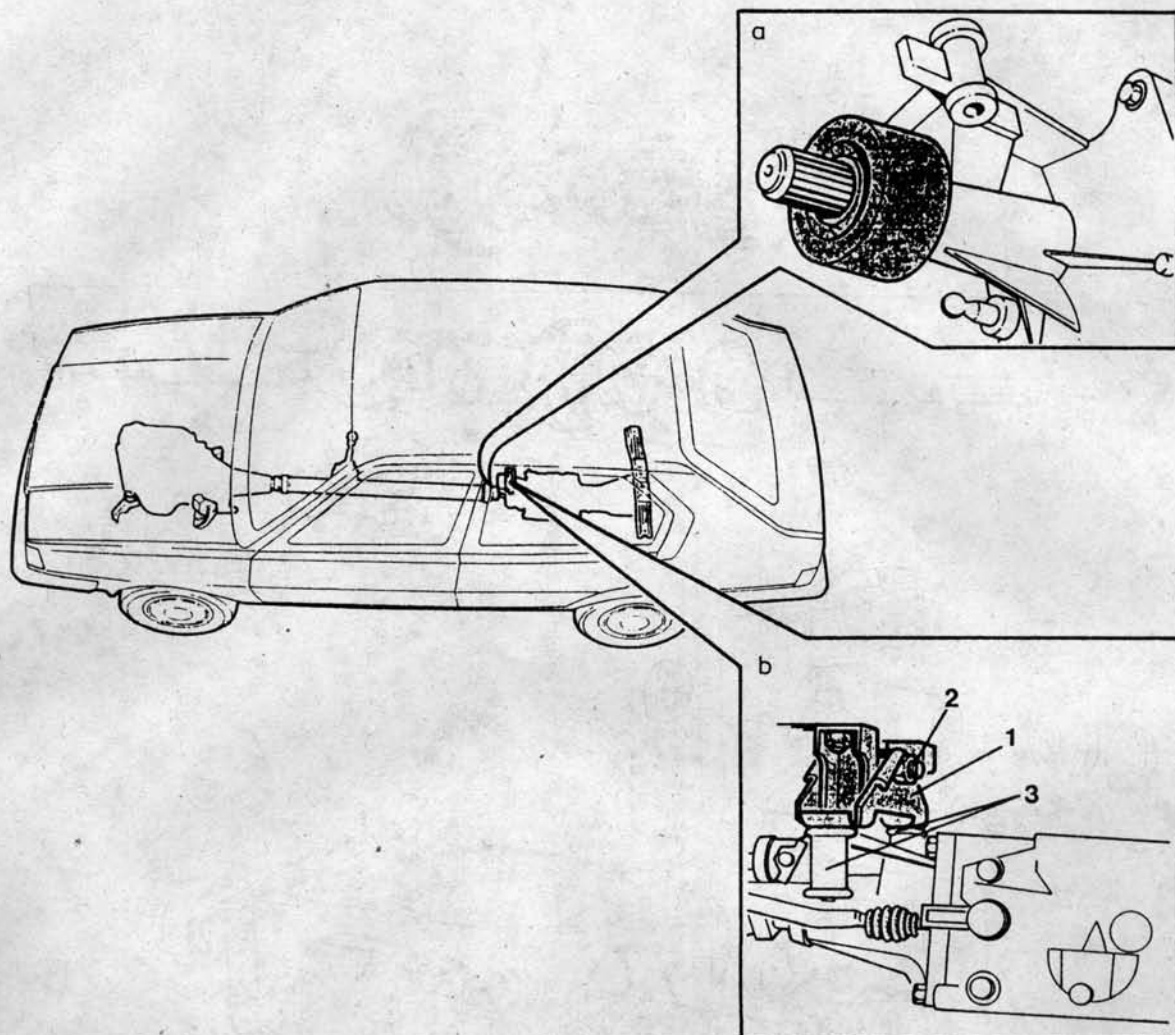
Гаситель крутильных колебаний в трансмиссии (а) и дополнительные элементы крепления КПП в автомобилях с двигателями D16 (б)
